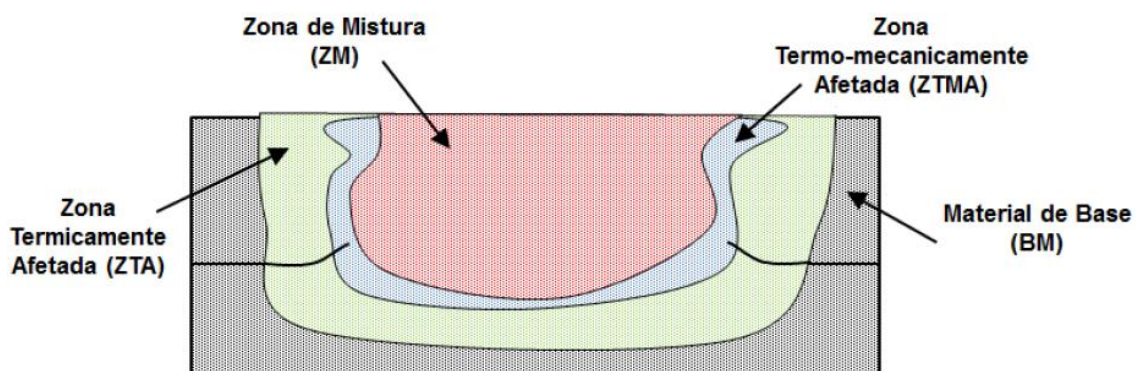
Desenho esquemático das diferentes regiões de soldagem de uma junta soldada pelo processo FSpW cortada na secção transversal [14].
